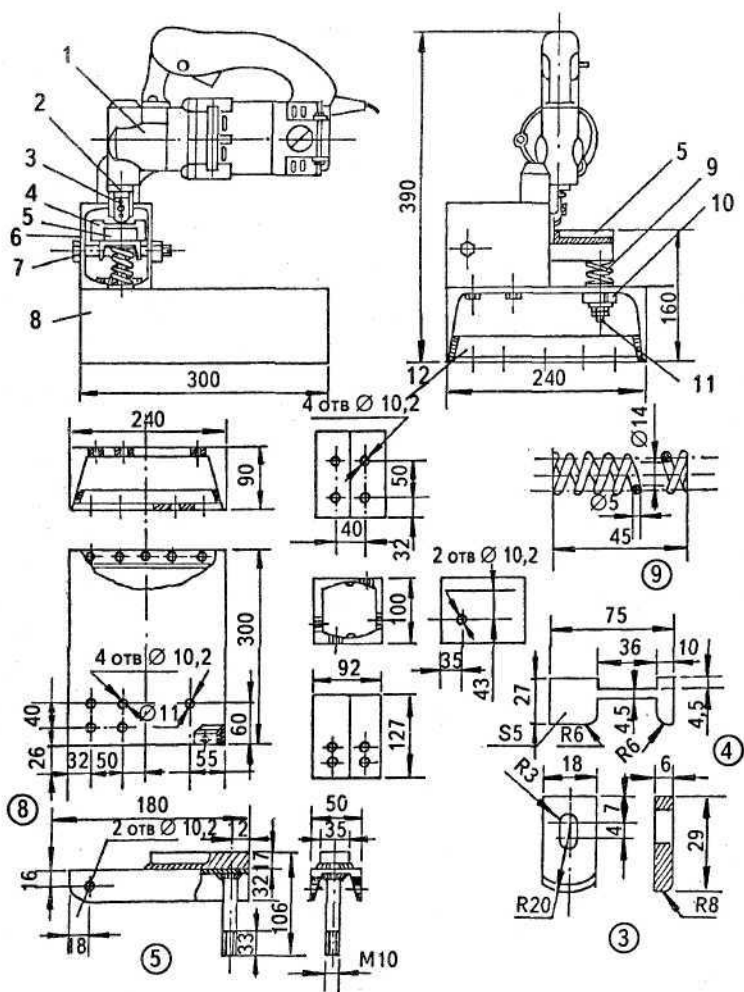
Самодельный верстак для механизированной отбивки кос: 1 — электропривод; 2 — вкладыши; 3 — блок; 4 — УПФ; 5 — наковальня; 6 — корпус; 7 — ось наковальни; 8 — станина; 9 — пружина; 10 — резиновая шайба; 11 — регулирующий болт; 12 — уголок
